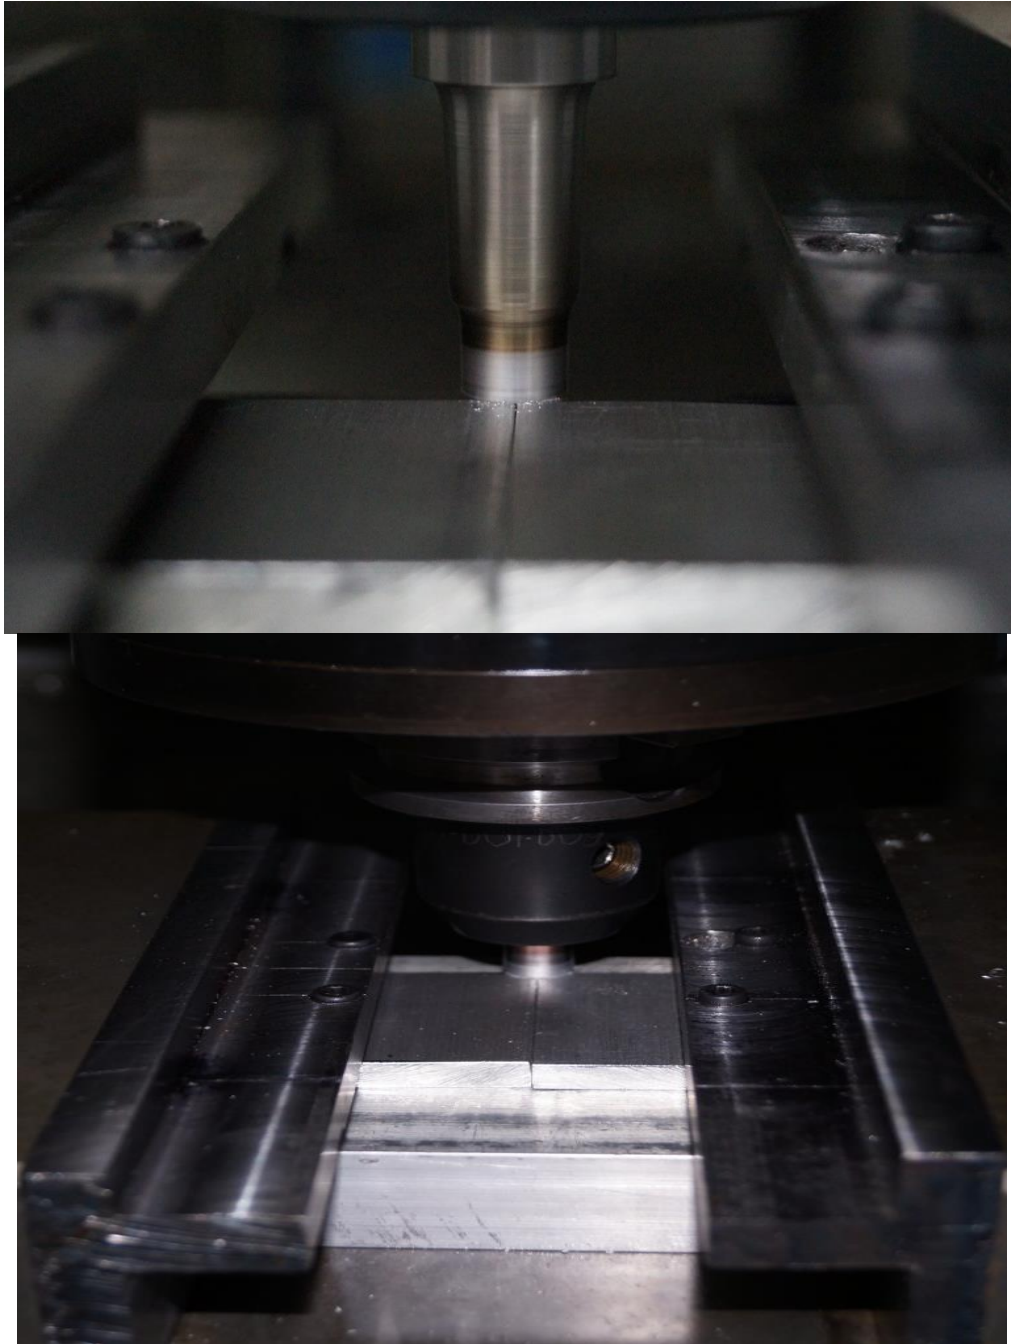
Hombro del indentador a roce con las placas a soldar.
